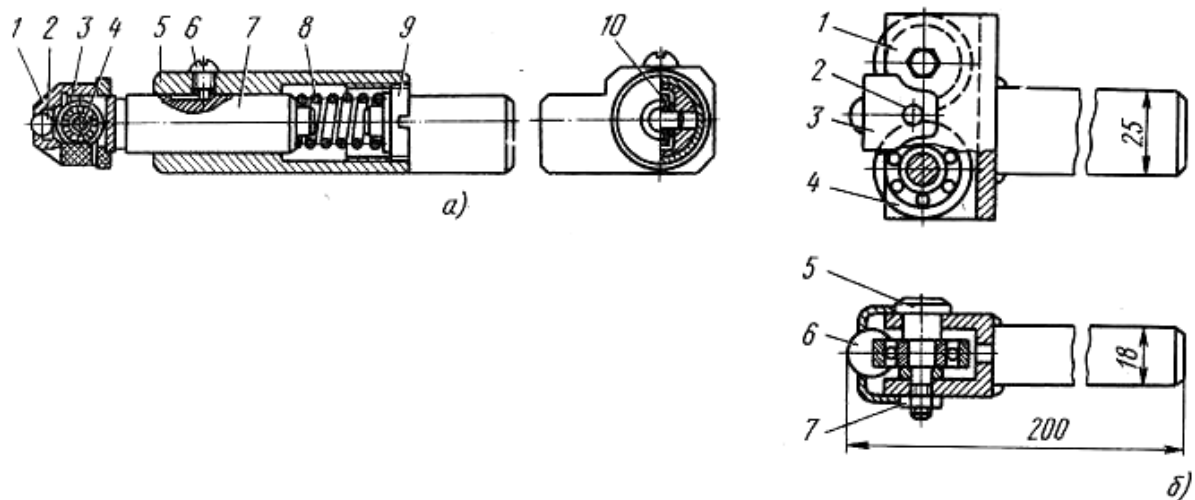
Інструменти для вигладжування поверхні кулькою [30]
